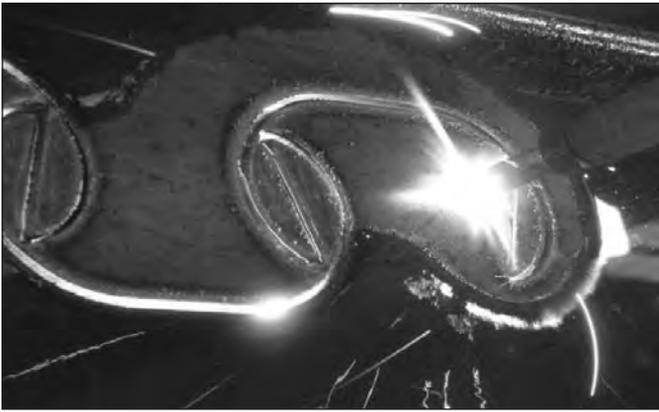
Fabrication de la découpe CL par oxycoupage d'un profilé
